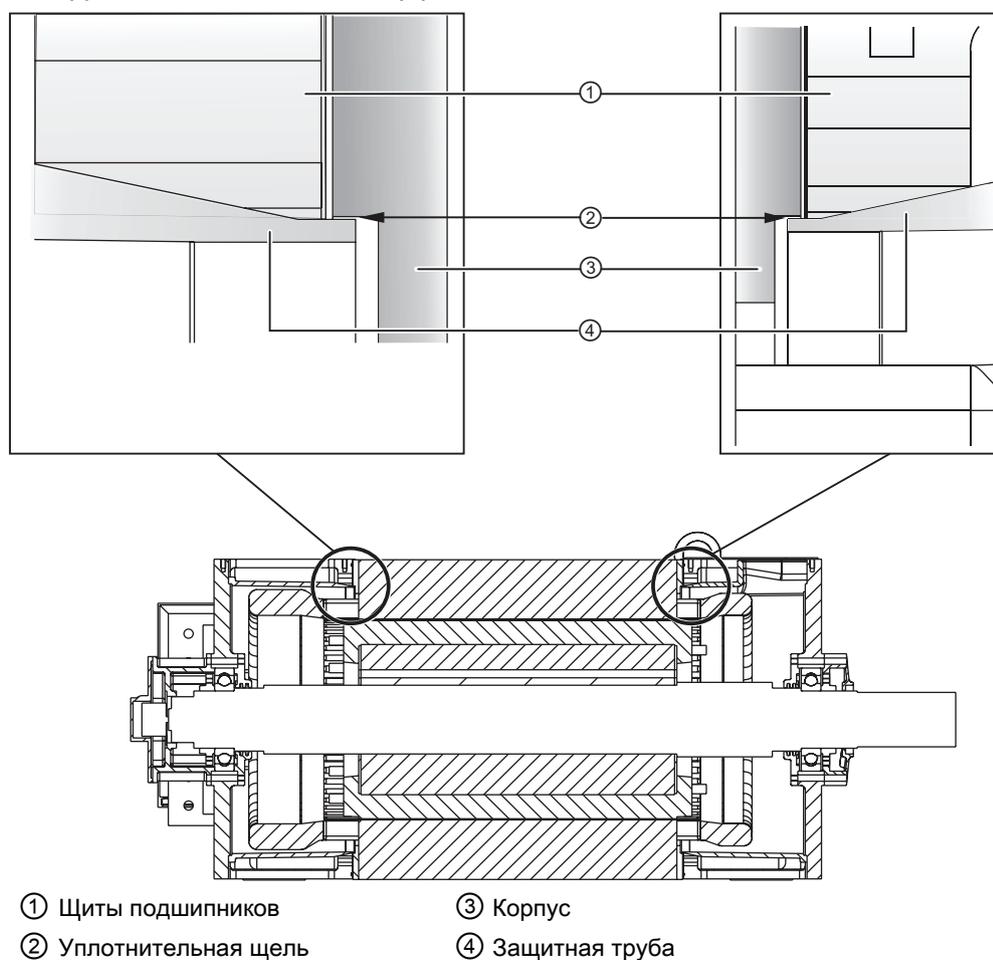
Уплотнительные зазоры между корпусом и щитами подшипников (принципиальная схема)
